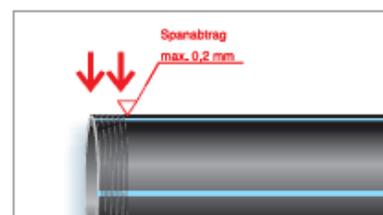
Spanende Bearbeitung im Schweißbereich, zuverlässig mit einem Rotationsschälgerät
